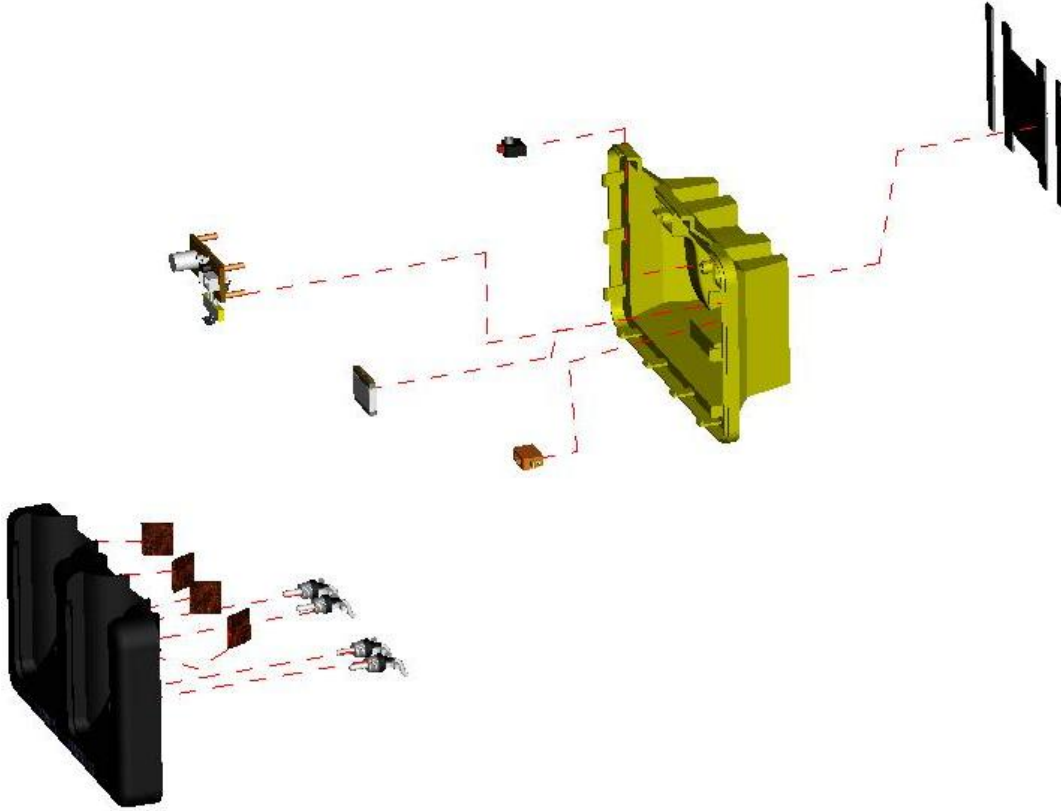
Vista de explosión de componentes del ensamble alojamiento.
